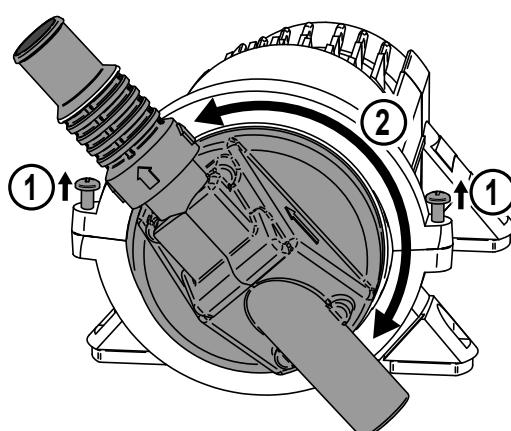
Rotierender Kopf der Pumpe Gulper 220
